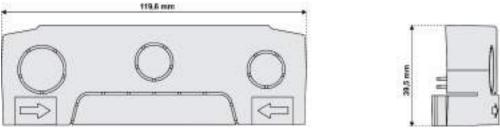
Dimensiones de la tapa de protección de las conexiones y cavidades separables
